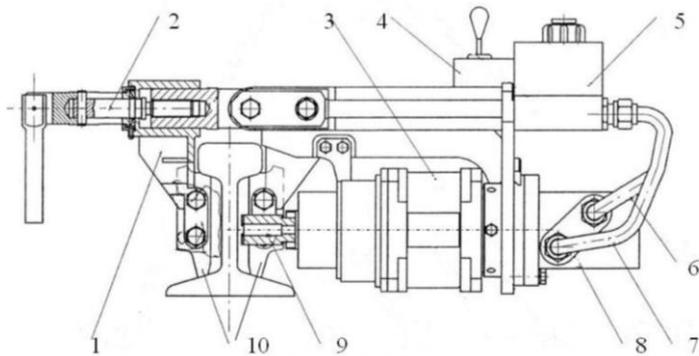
Станок рельсоверлильный СРГ-12:1 – упор-захват, 2 – винтовое зажимное устройство с рукояткой, 3 – гидроцилиндр, 4 – гидрораспределитель, 5 – регулятор расхода, 6, 7 – трубопровод, 8 – гидродвигатель, 9 – сверло ИС/420, 10 – съемные шаблоны
